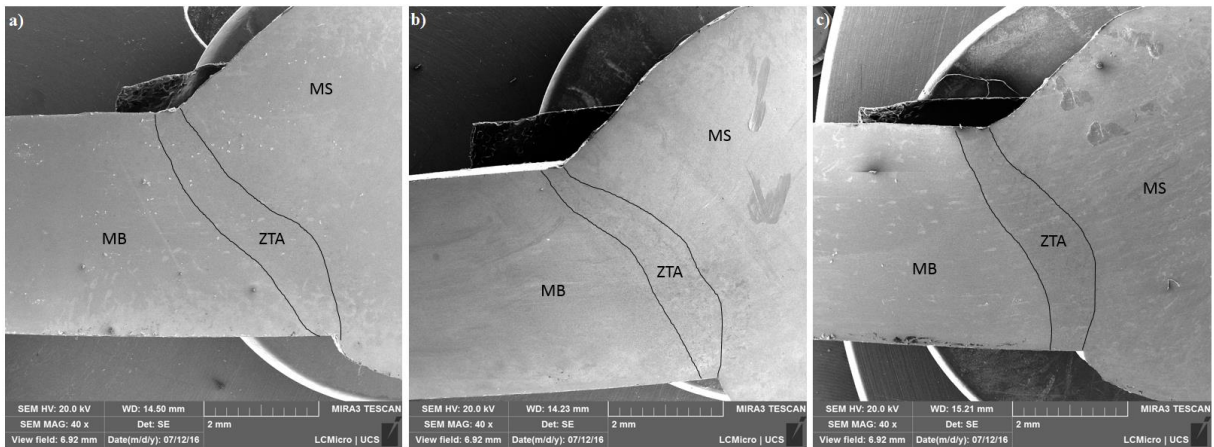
Imagens microscópicas das juntas soldadas com energias de soldagem utilizadas durante o ensaio B01 (a), B02 (b) e B03 (c)
